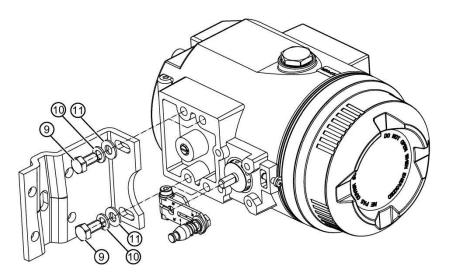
Установка с монтажным кронштейном, взрывобезопасный корпус
